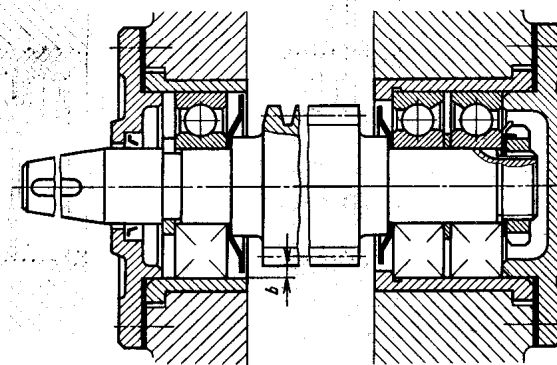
Вал установлен на двух радиально-упорных шарикоподшипниках; левый подшипник – «плавающий»
